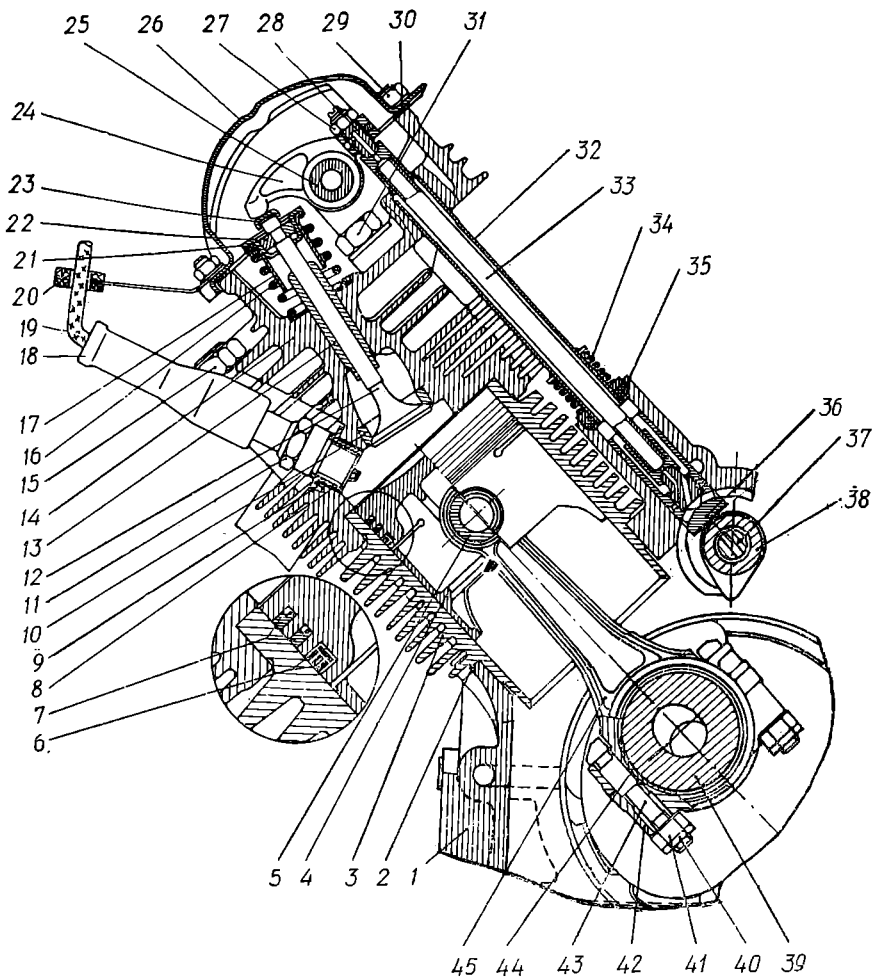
Кривошипно-шатунный и газораспределительный механизмы:
